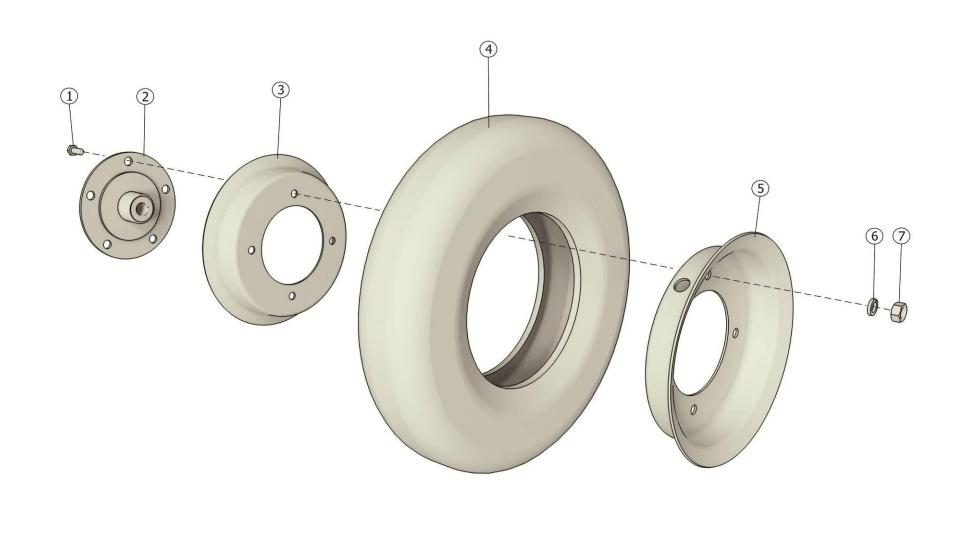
Колесо в сборе МЗС-90.01.100
